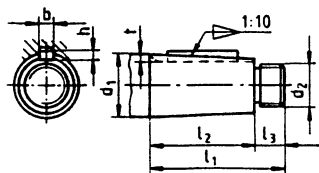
Kegelige Wellenenden mit Außengewinde
